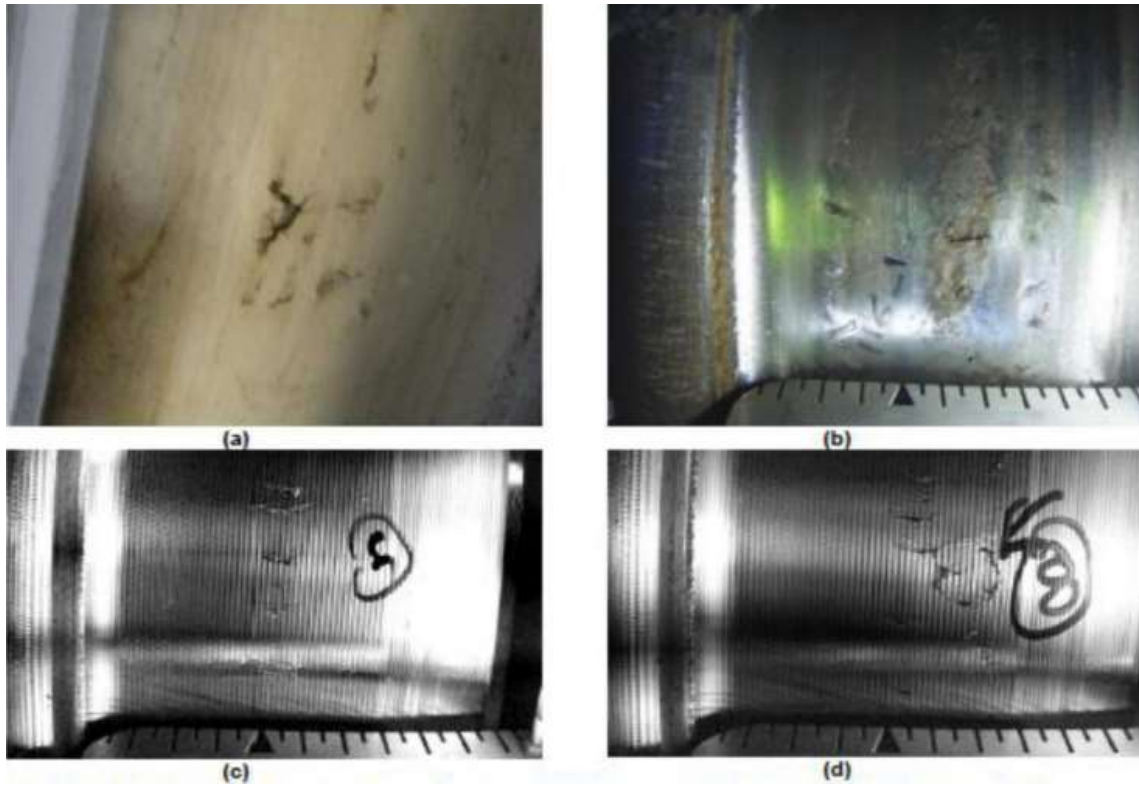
En a) y b) se muestra RCF Clusters antes de reperfilado. En c) y d) las fisuras aparecen más largas, más ensanchadas o más visibles durante el reperfilado, [21]
